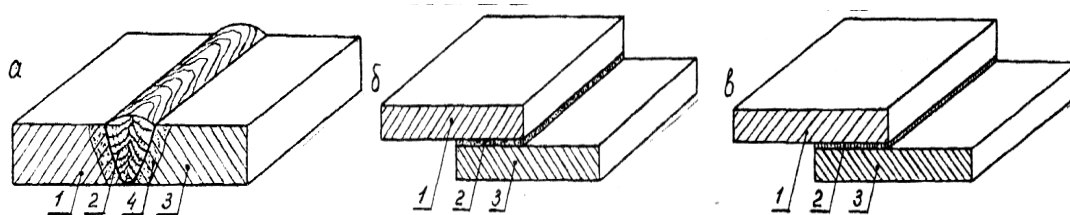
Неразъемные соединения, получаемые сваркой (а), пайкой (б), склеиванием (в). 1,3 - основной металл; 2 - шов; 4 - зона термического влияния (а)
